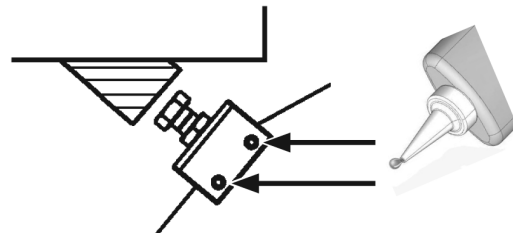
Für die Befestigungsschrauben Loctite 243 oder Gleichwertiges verwenden
